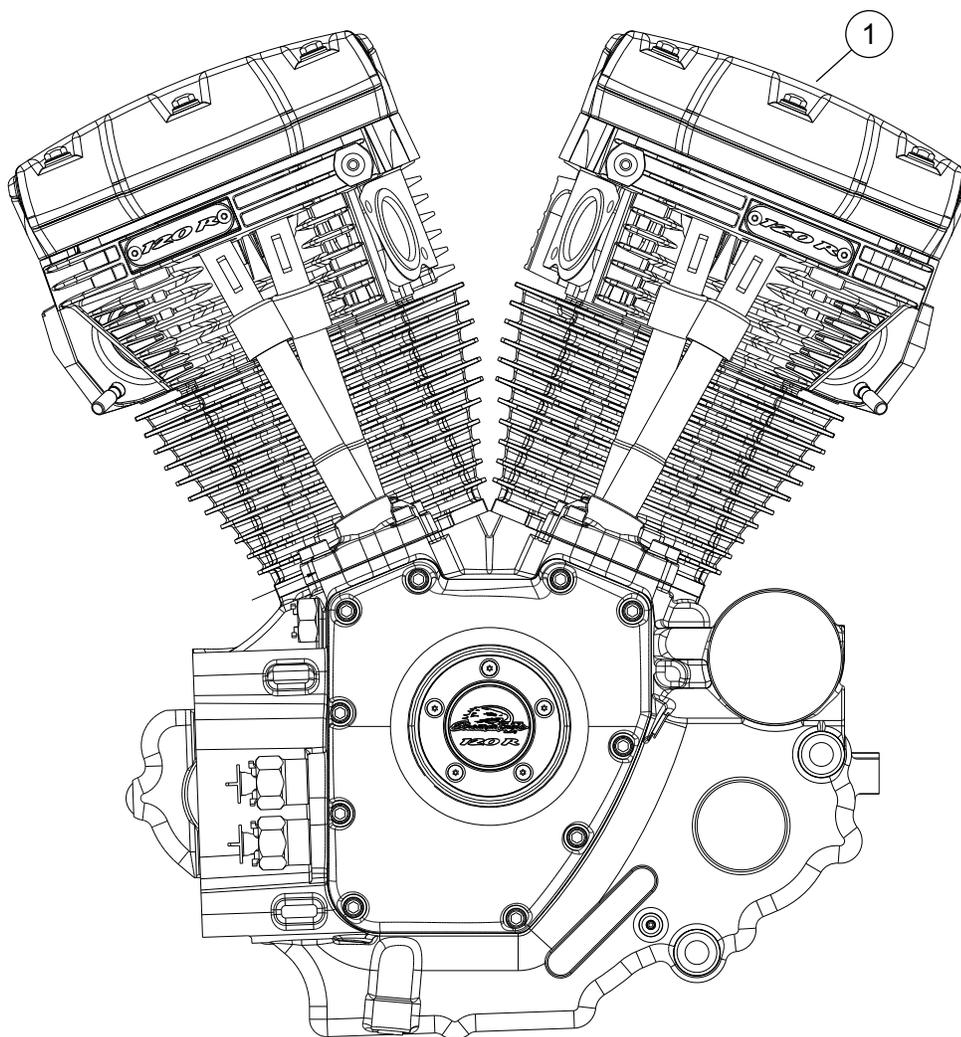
Ensemble moteur, Moteur complet Screamin' Eagle Pro 120R (Beta)
